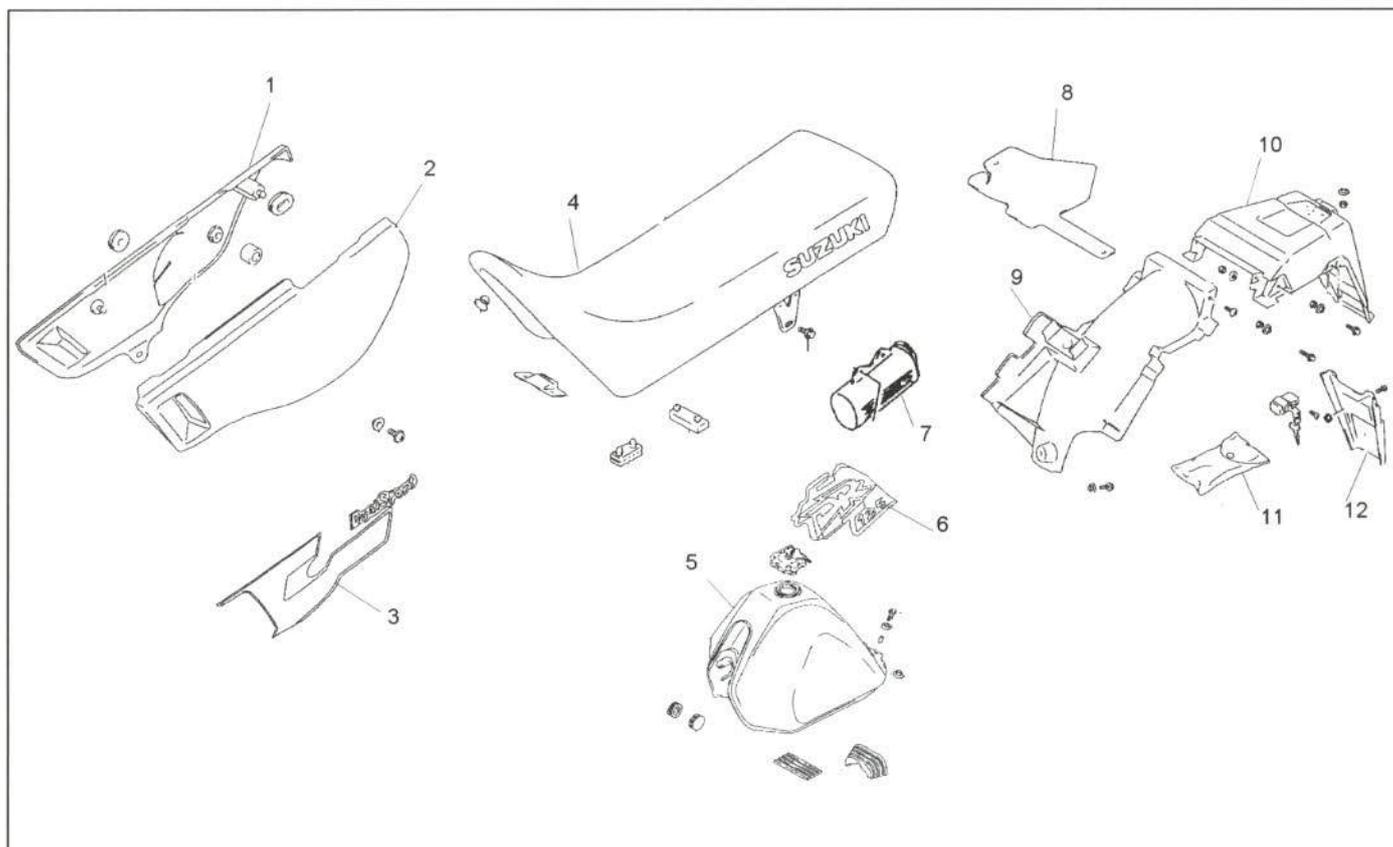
Despiece de las piezas exteriores de la parte trasera
